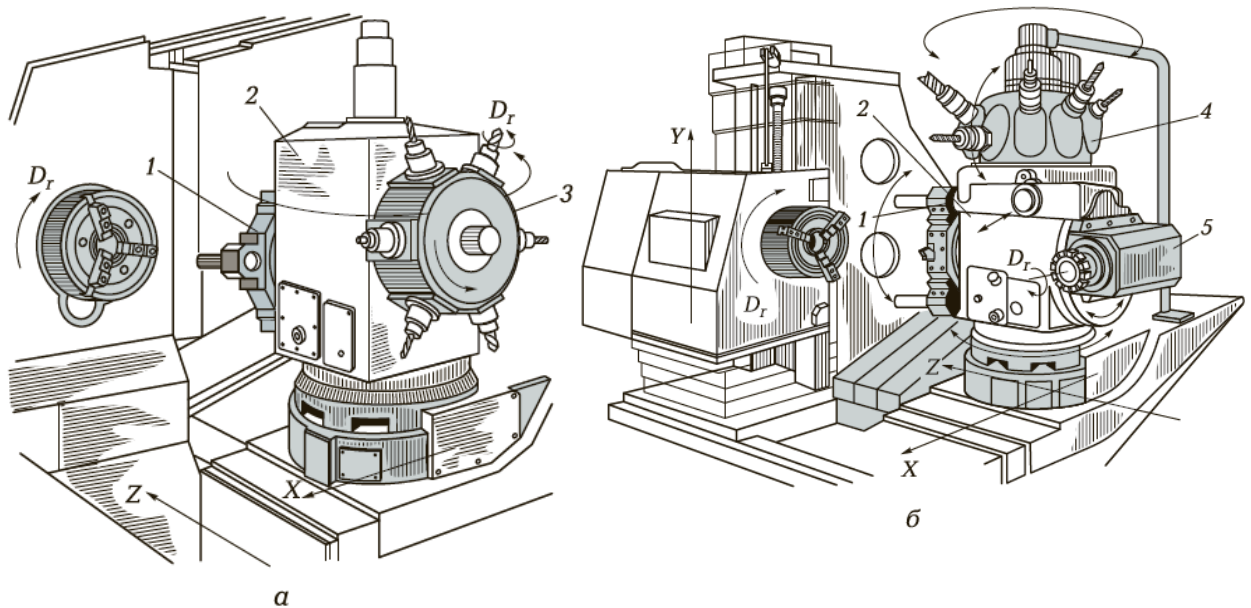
Инструментальные узлы МС с револьверными головками (а) и с магазином инструментов, револьверной и инструментальной головками (б):
